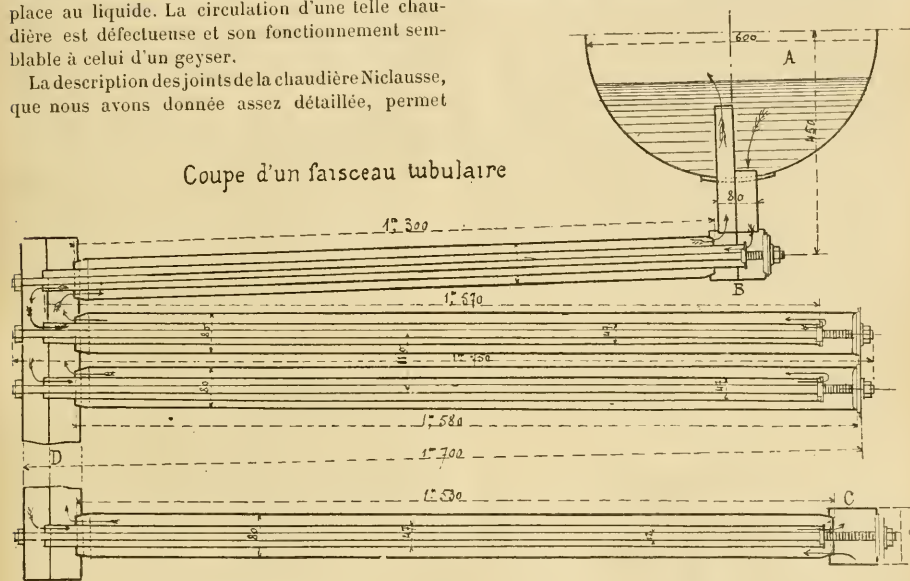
Coupe d'un faisceau tubulaire du générateur Collet. — A, réservoir supérieur; D, collecteur.
